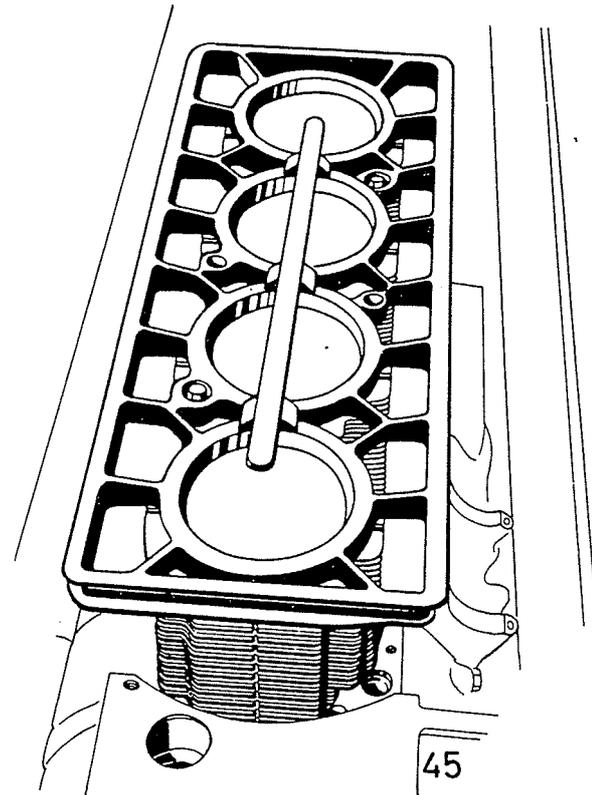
Vorrichtung zur Halterung der Zylinder auf dem Motorgehäuse
